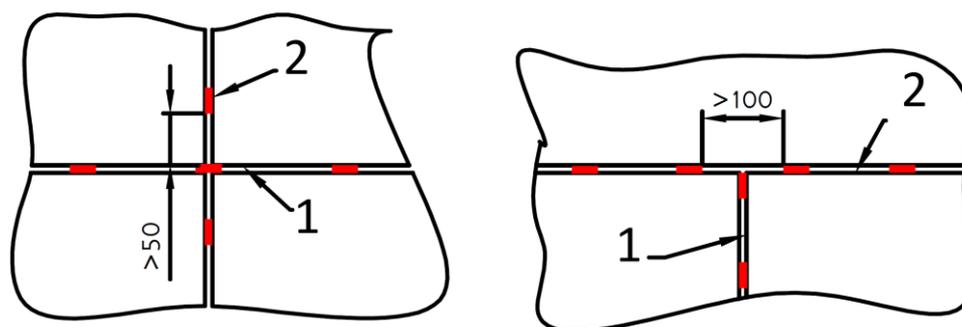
Очередность установки прихваток (1,2) на пересечении сварных соединений.
